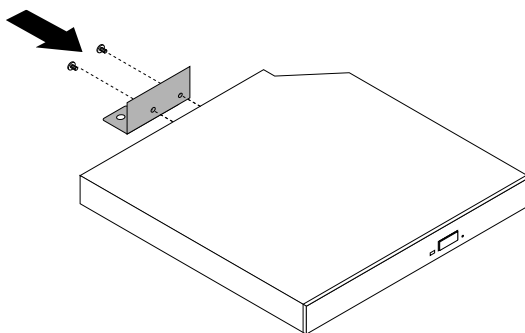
Установка металлической пластины внешнего дисковод для оптических дисков
